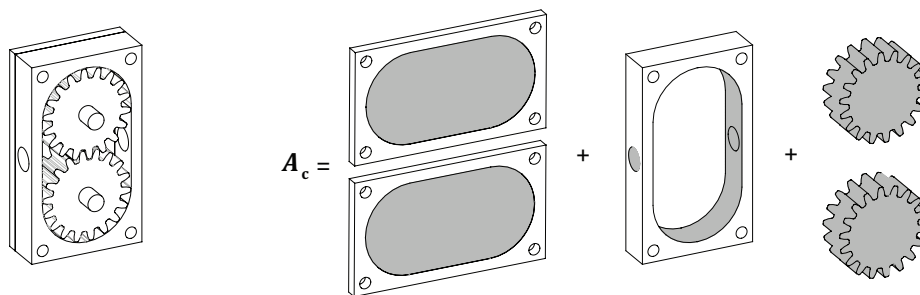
Surface mouillée d'une pompe hydraulique à engrenages externes
